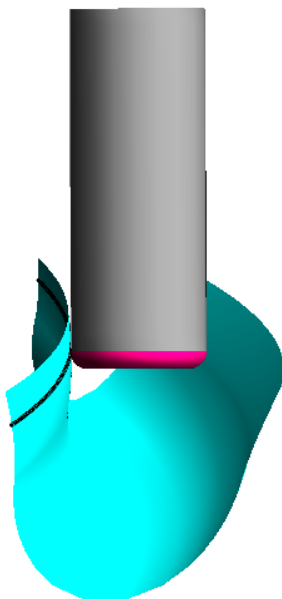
Фрагмент поверхности зуба колеса в касании с торической фрезой
